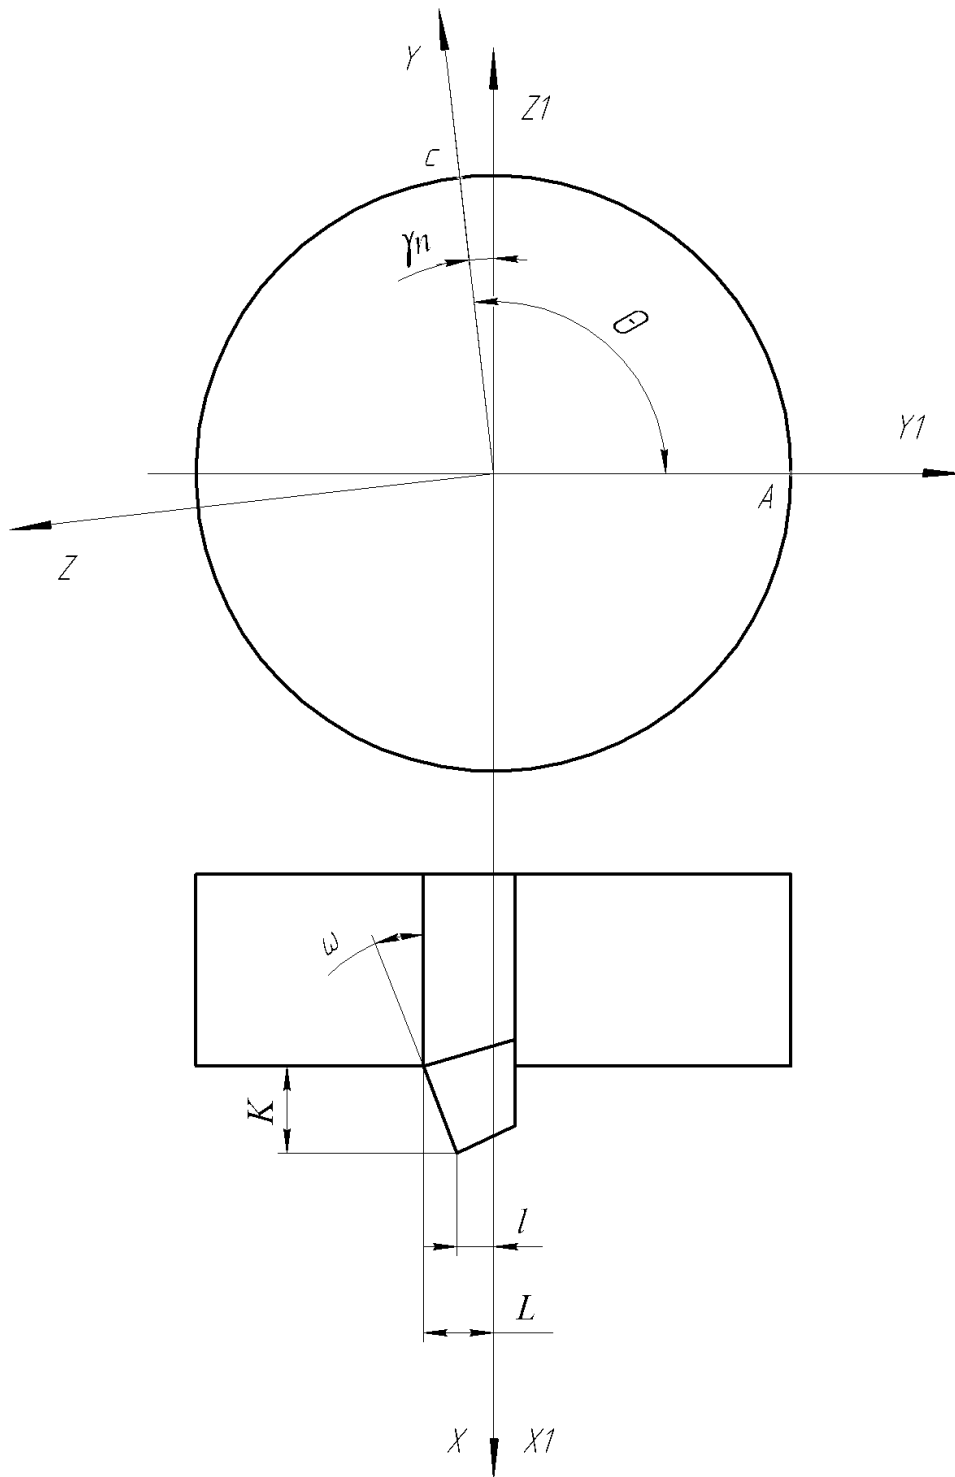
Положення паза збірної торцевої фрези
